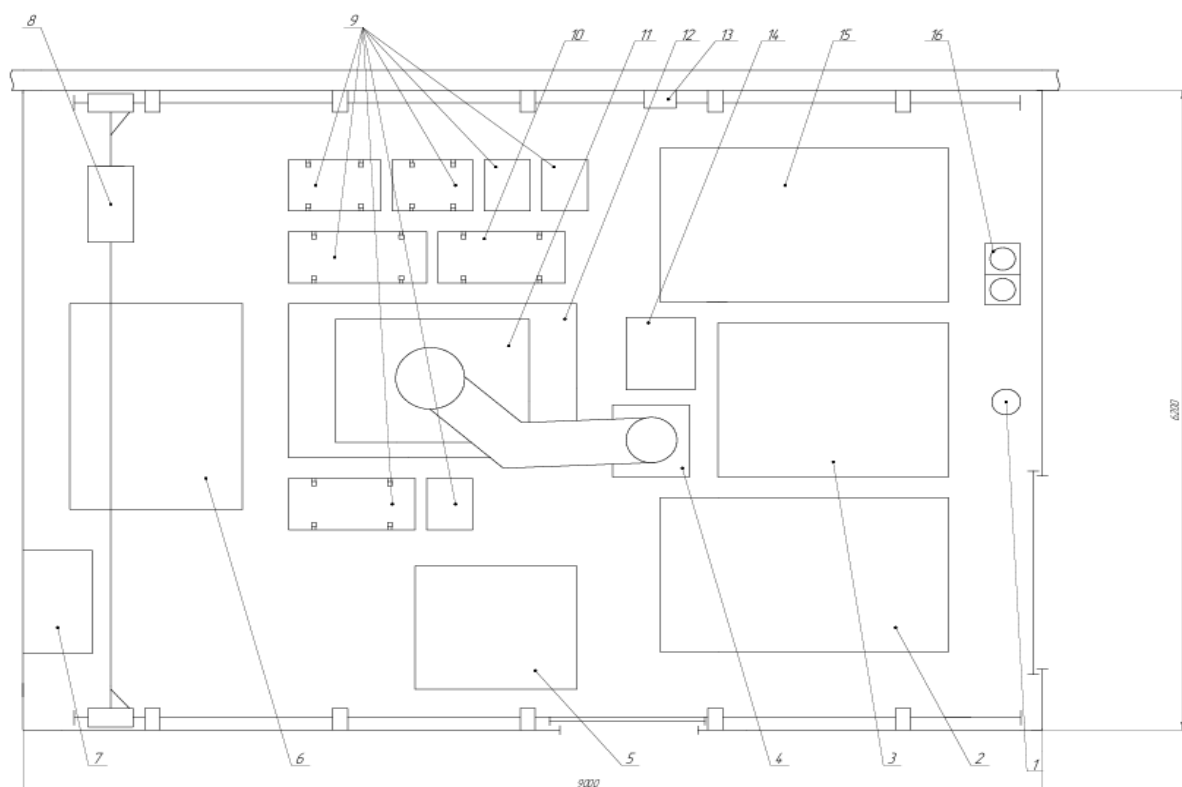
Схема планування робочого місця (план цеху)
